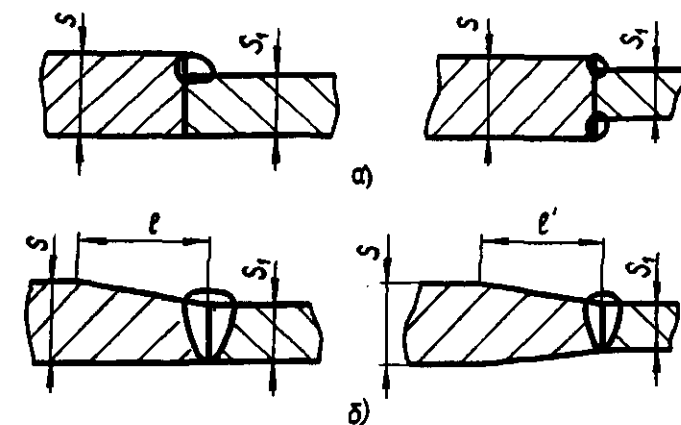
Сварные ступенчатые заготовки: а – нетехнологичные; б – технологичные
